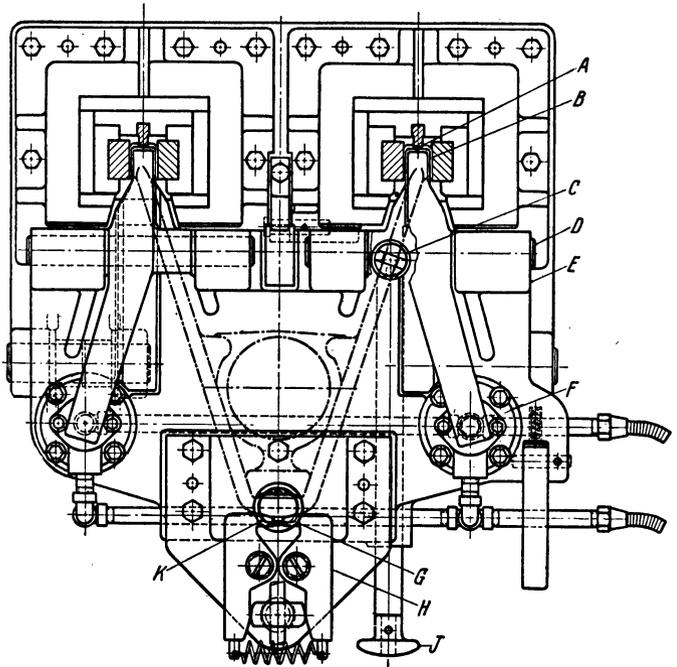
Aufsicht einer Außenräumvorrichtung mit Preßluftspannung.
